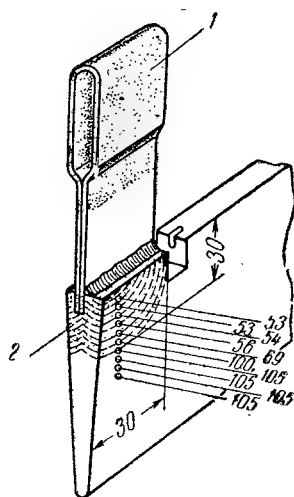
Изменение твердости H_B пластины после пайки припоем ПМФ7:
